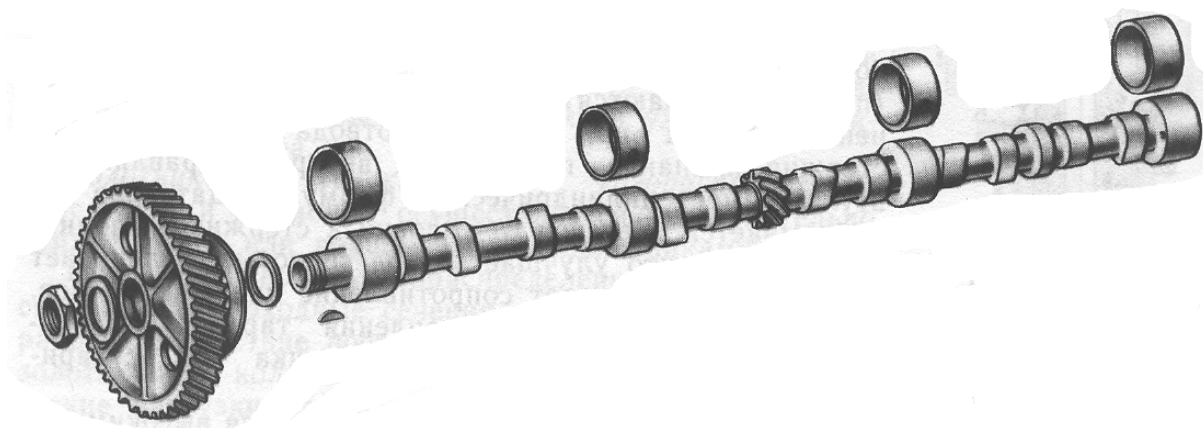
Розподільний вал, ведуча шестерня і підшипники
